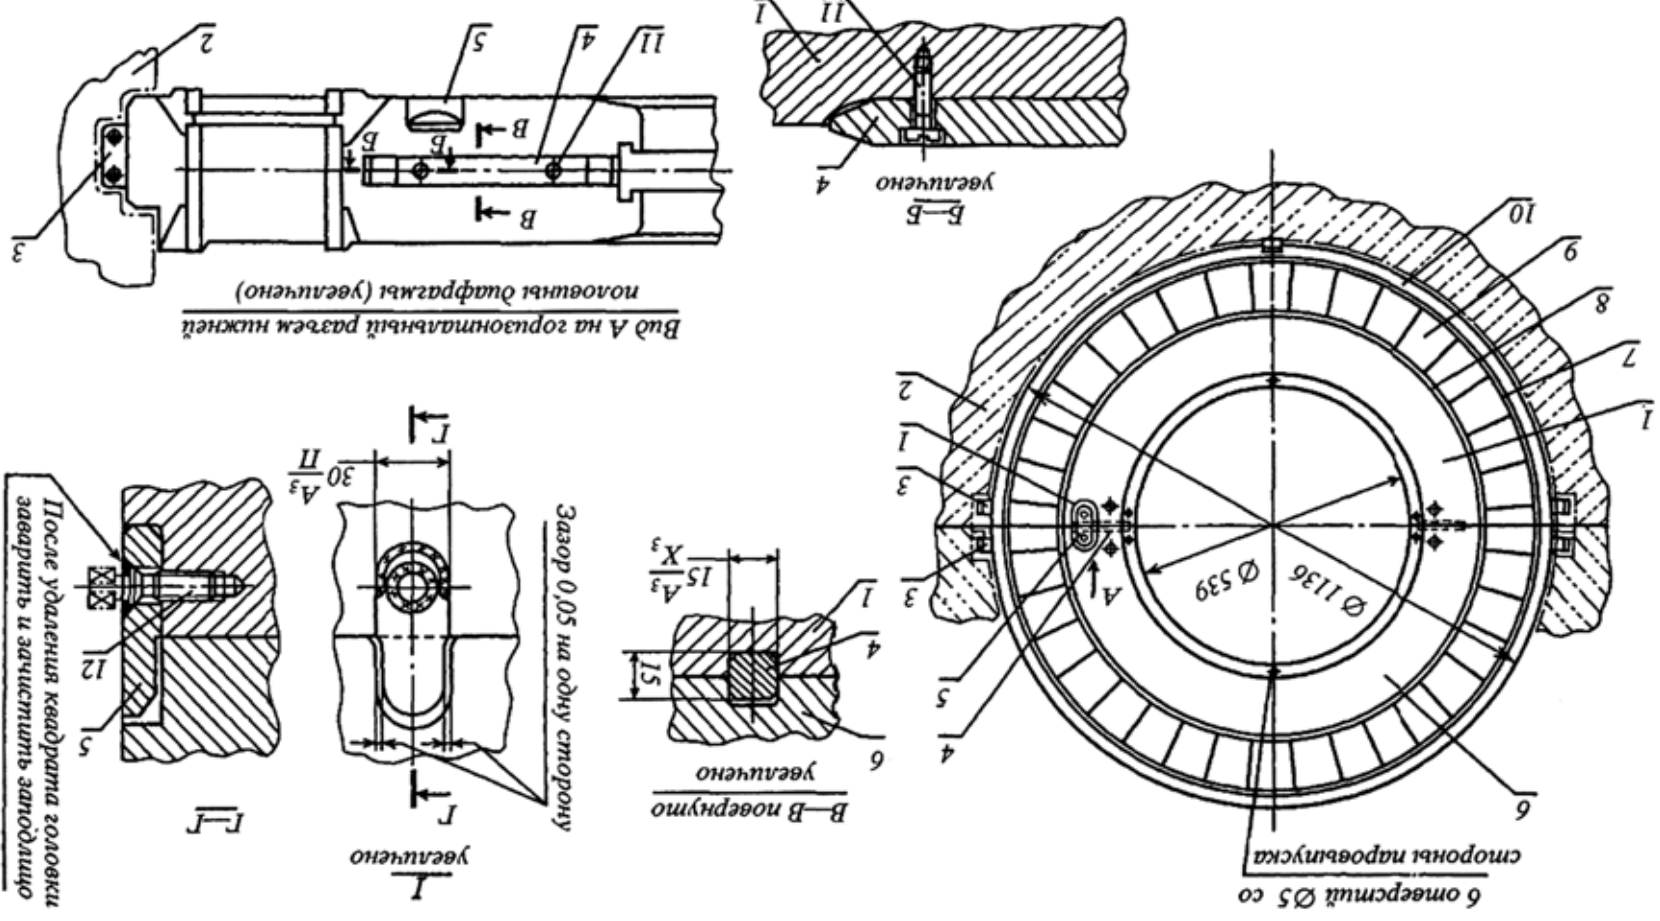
Стальная сварная диафрагма турбины К-300-240 ЛМЗ:
